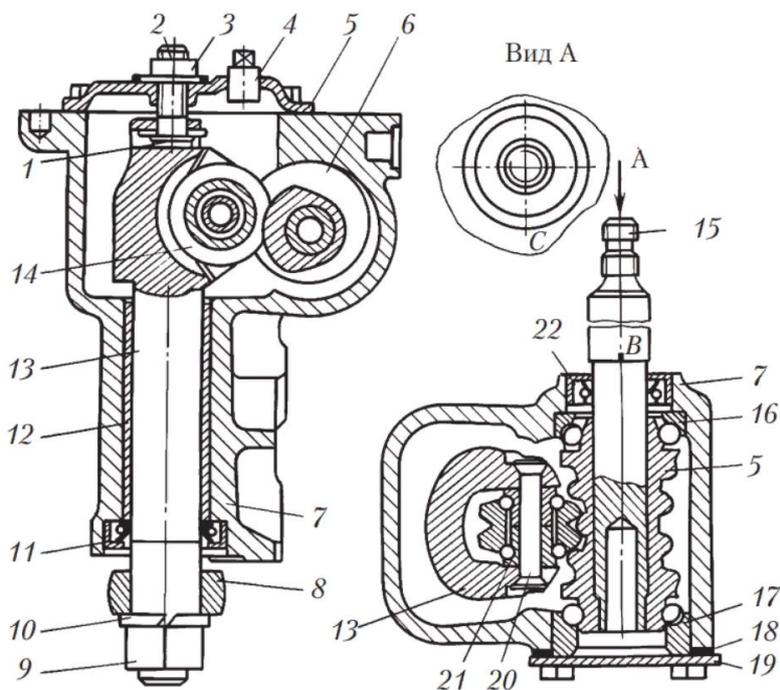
Схема рулевого механизма типа червяк-ролик: 1 — пластина регулировочного винта вала сошки; 2 — регулировочный винт; 3 — контргайка; 4 — пробка; 5 — крышка картера рулевого механизма; 6 — червяк; 7 — картер рулевого механизма; 8 — сошка; 9 — гайка крепления сошки; 10 — пружинная шайба; 11 — сальник вала сошки; 12 — втулка; 13 — вал сошки; 14 — ролик вала сошки; 15 — вал червяка; 16, 17 — подшипники червяка; 18 — регулировочные прокладки; 19 — нижняя крышка картера; 20 — ось ролика; 21 — подшипник ролика; 22 — сальник вала червяка; В, С — метки
